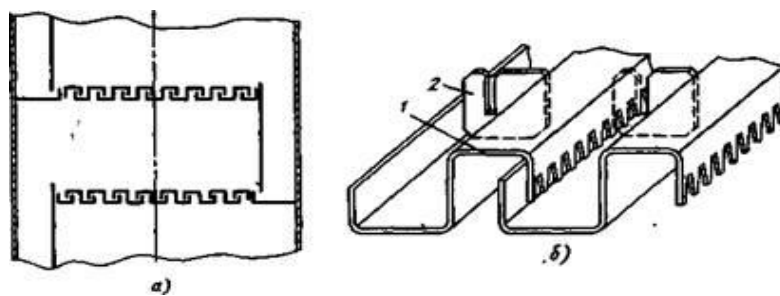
Тарелка с S-образными элементами: а — общий вид; б—
